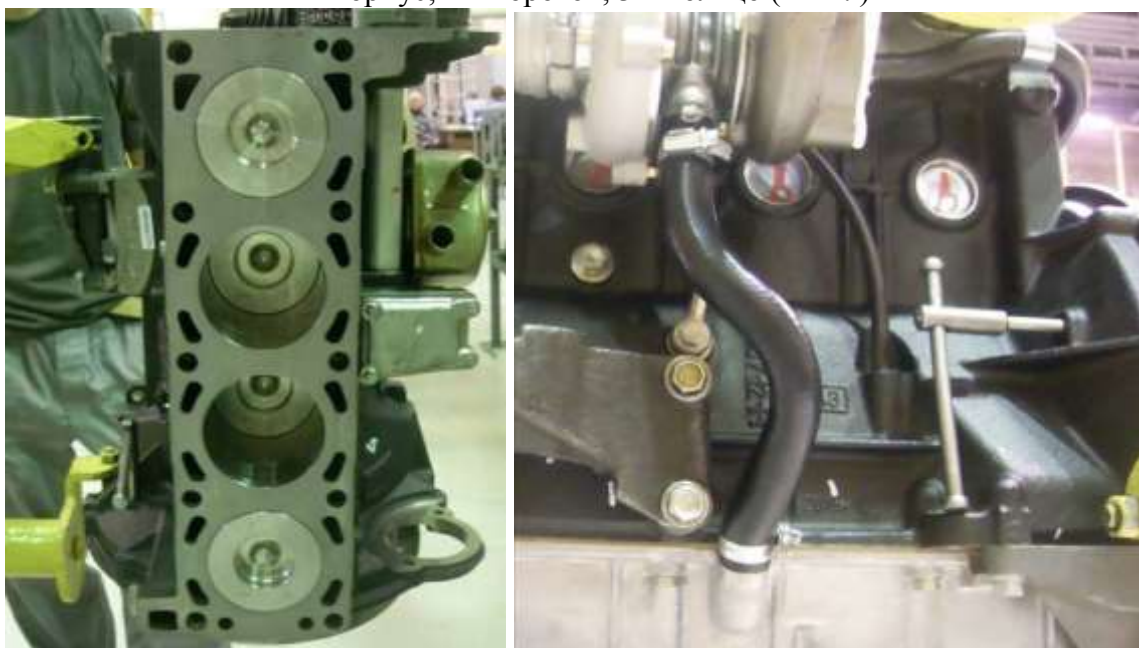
ЗМ 7820-4582 Штифт установочный коленчатого вала:
